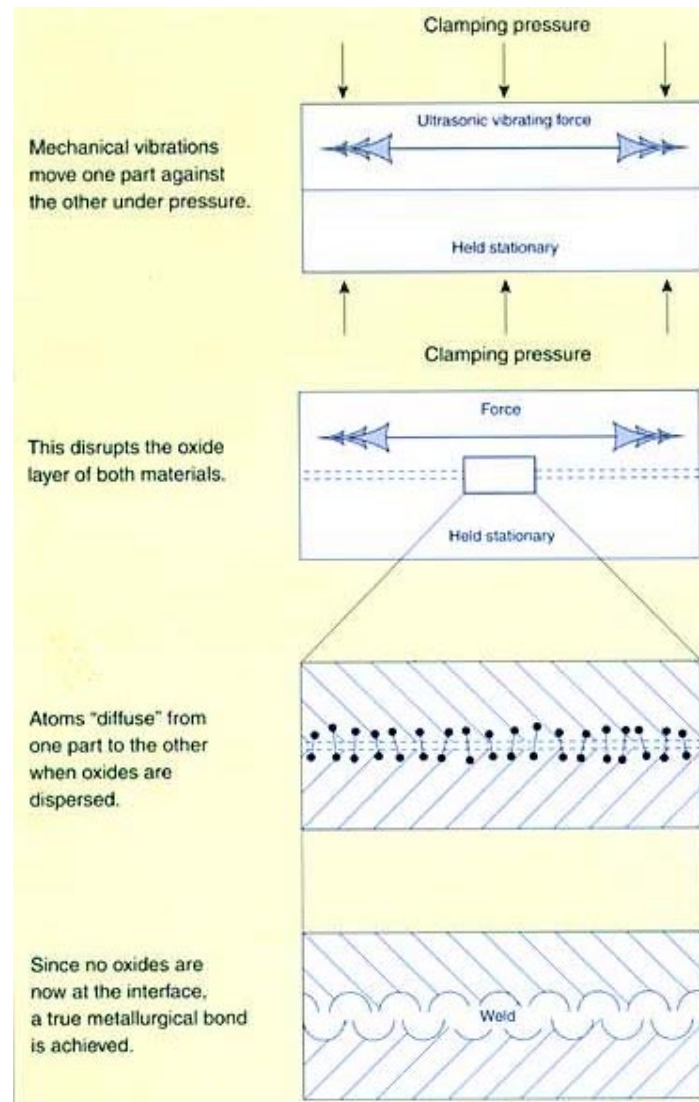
Mecanismos da soldagem de metais por ultra-som.
